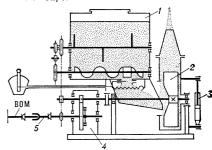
Схема тракторного универсального опыливателя: 1 — бункер с мешал-кой и питателем; 2 — вентилятор; 3 — гидроцилиндр для изменения угла наклона распыливающего наконечника; 4 — редуктор; 5 — карданная передача.
